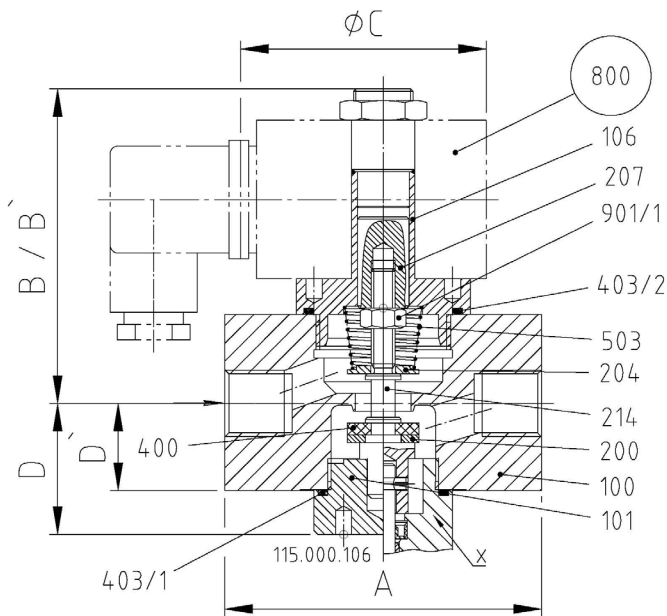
Gewindeausführung: 1-EVO 3-10R; 4- EVO 2-7R
